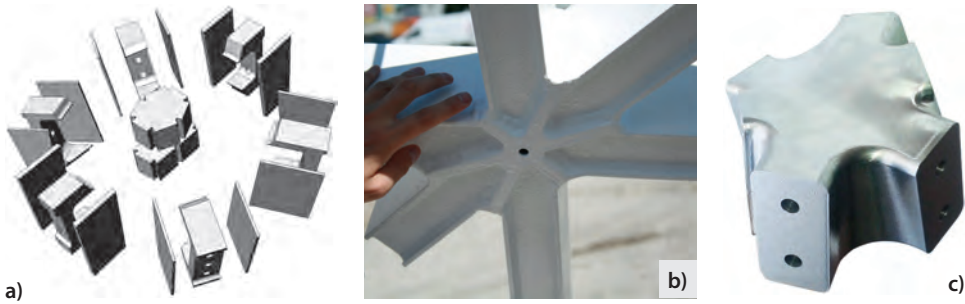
a) geschweißter Knoten (© seele), b) gebrannter Knoten (© Wagner Biro) und c) Vollknoten (© Metal Yapi)
